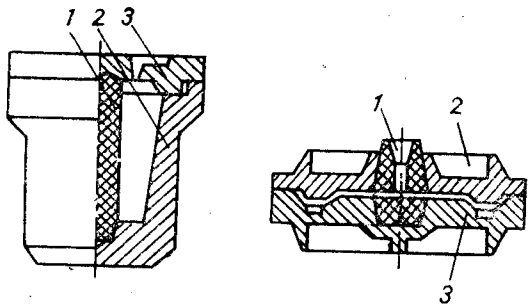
Металеві форми (кокілі) для виготовлення виливків корпуса (а) та диска (б): 1 — шишка; 2, 3 — частини форми.
